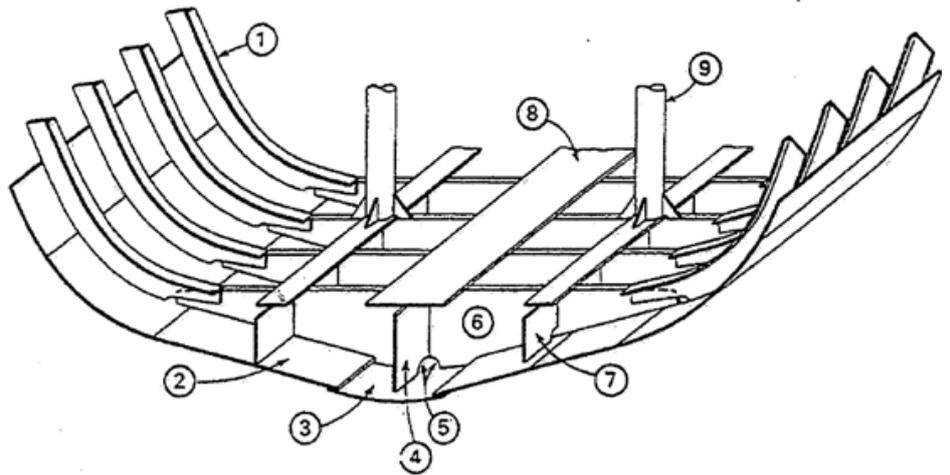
Construction de la charpente de fond simple (sans plafond du double fond).
